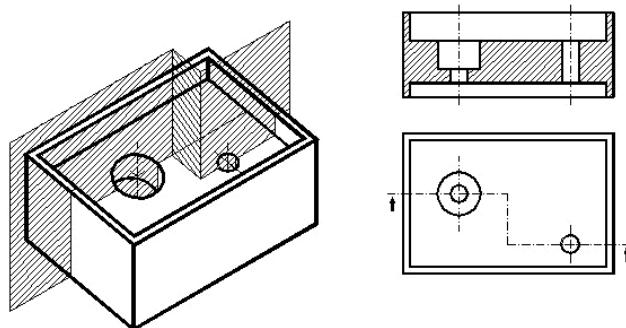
Adoção de um plano de corte adequado, mediante translação e apresentação das projeções ortogonais.
